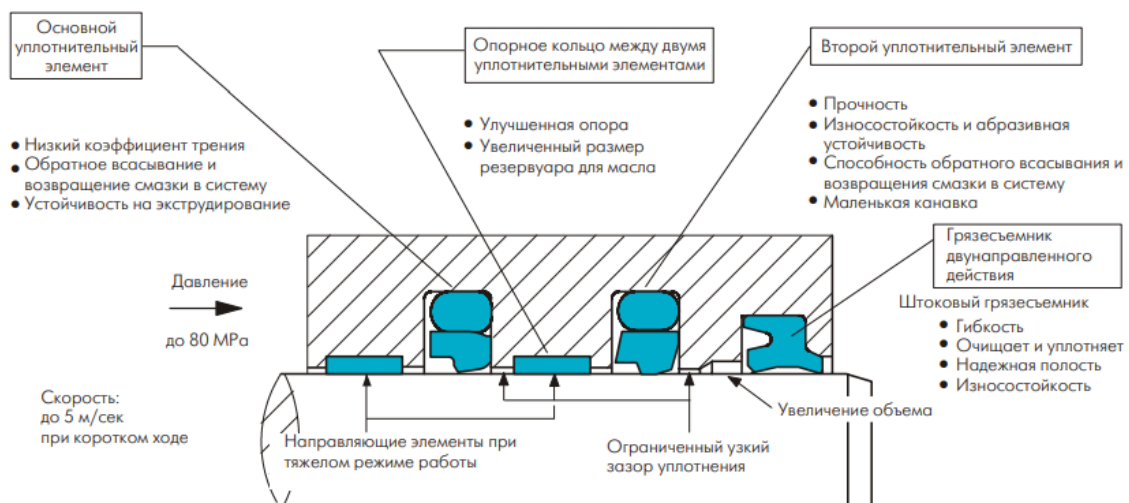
Классическая схема конструкции уплотнения штока [25]
